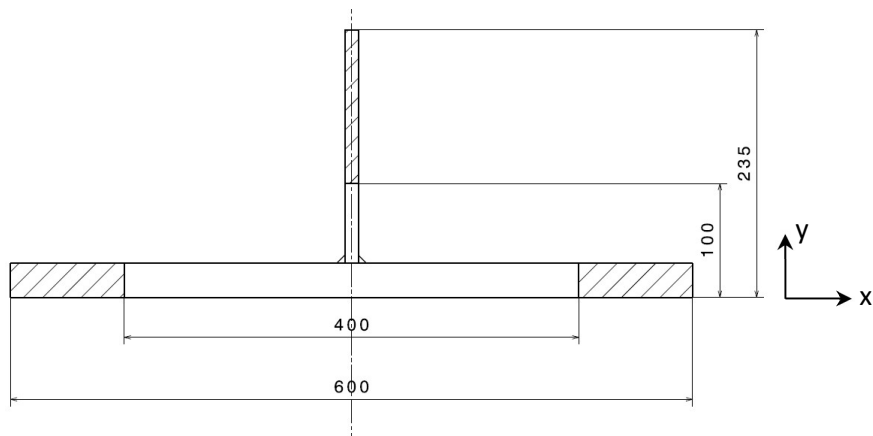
Découpe des extrémités de la maquette « passes décalées » - dimensions en (mm)
